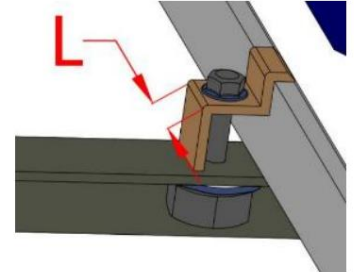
e tabela: posição de instalação do módulo solar de células de 210 mm e tipo de módulo com 4 braçadeiras no lado comprido
